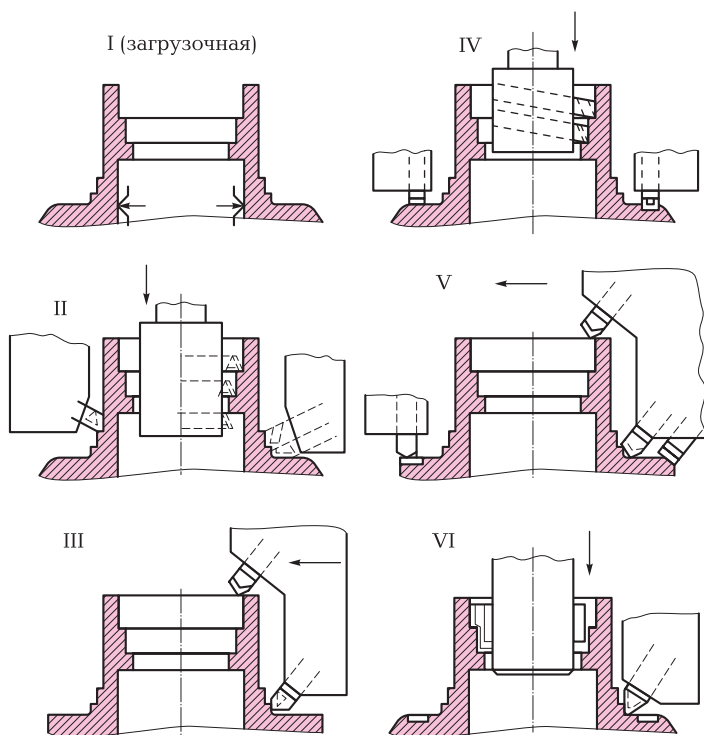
Технологическая схема обработки заготовки на вертикальном шестипозиционном полуавтомате
